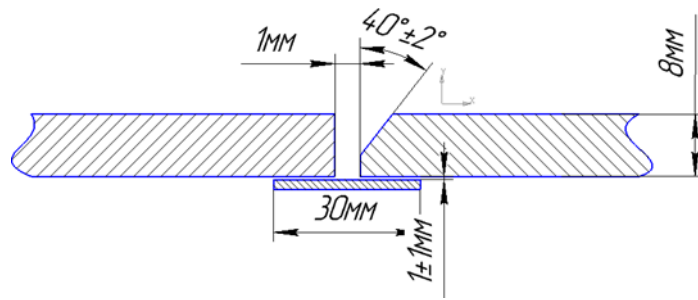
Вид подготовки кромок приварки окрайки днища
